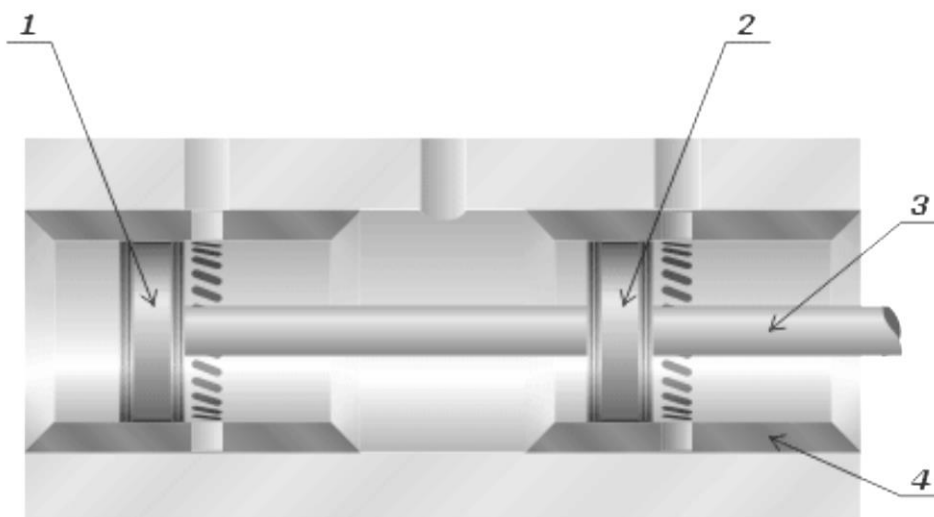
Принципова схема прецизійної золотникової пари розподільного пристрою: 1, 2 – запірні штоки; 3 – золотник; 4 – корпус
